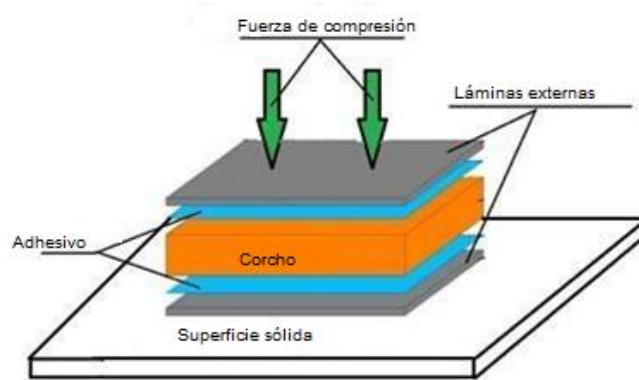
Diagrama esquemático del proceso de fabricación de un panel plano estructurado en sándwich.
